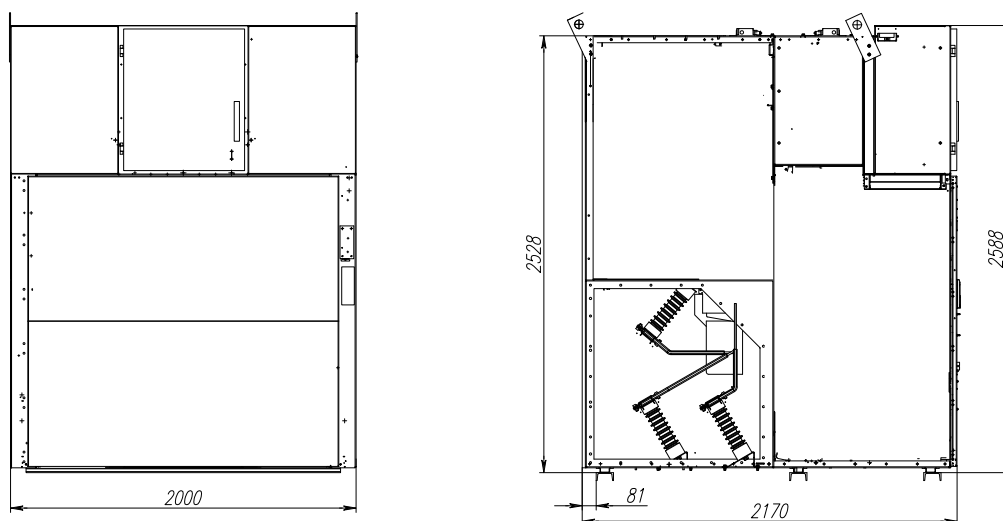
Общий вид и габаритные размеры шкафа с ТЧН
